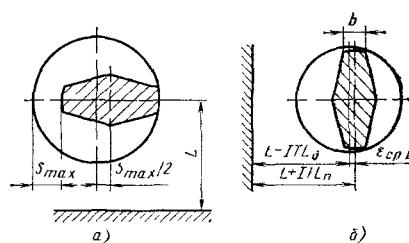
Расчетные схемы бокового зазора (а) и ширины b ленточки срезанного пальца (б) при установке заготовки цилиндрическим отверстием на срезанный палец
